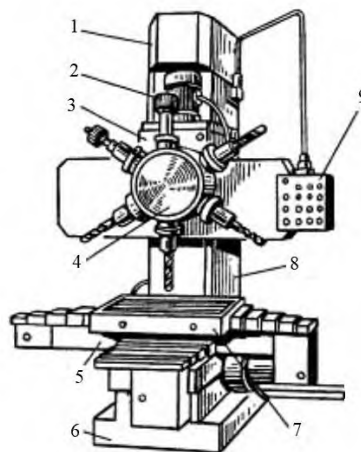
Розташування основних частин свердлильного верстату 2P135Ф2 (1 – редуктор подачі; 2 – коробка швидкостей; 3 – шпиндельна бабка; 4 – револьверна головка; 5 – салазки столу; 6 – станина; 7 – хрестовий стіл; 8 – колона; 9 – підвісний пульт керування)
